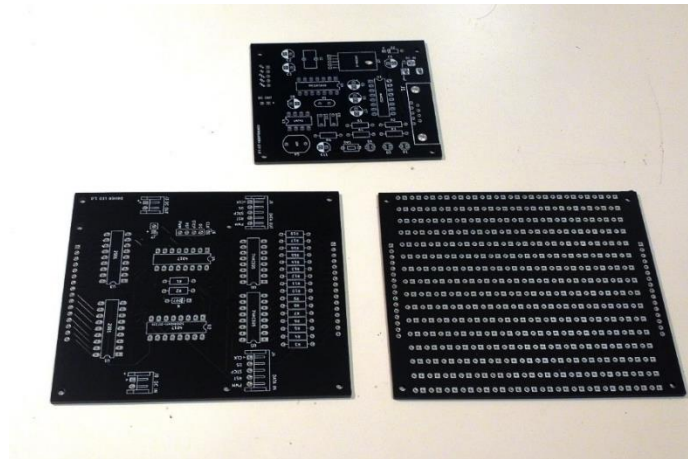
Placas PCB (microcontrolador, driver y panel LED)
